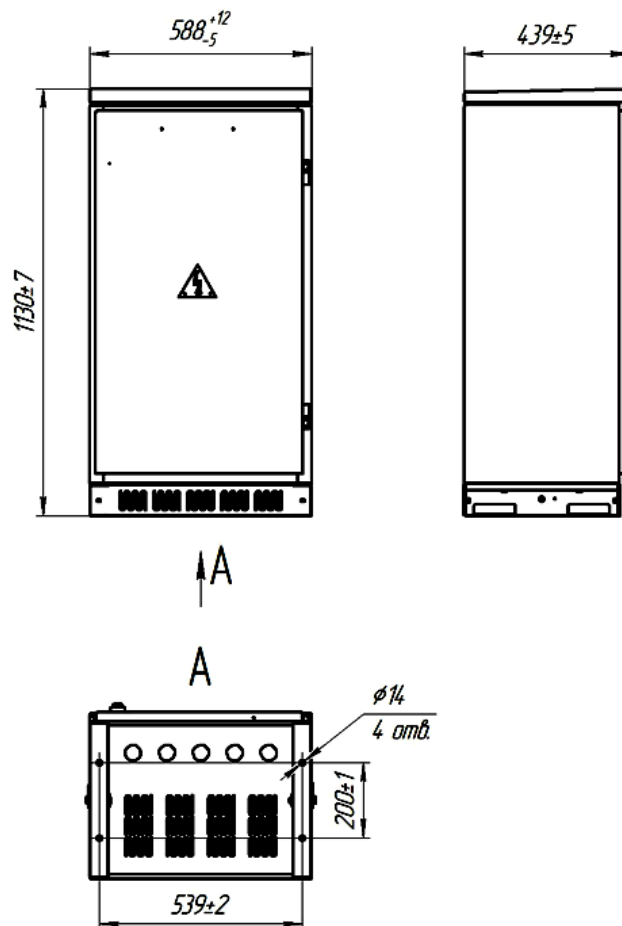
Общий вид и габаритные размеры ДРП
